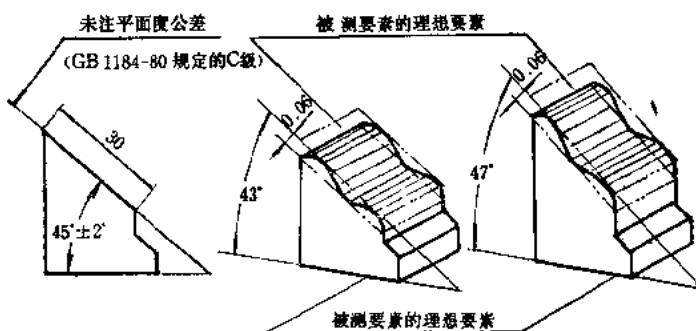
采用独立原则的角块其平面度公差与角度公差无关
